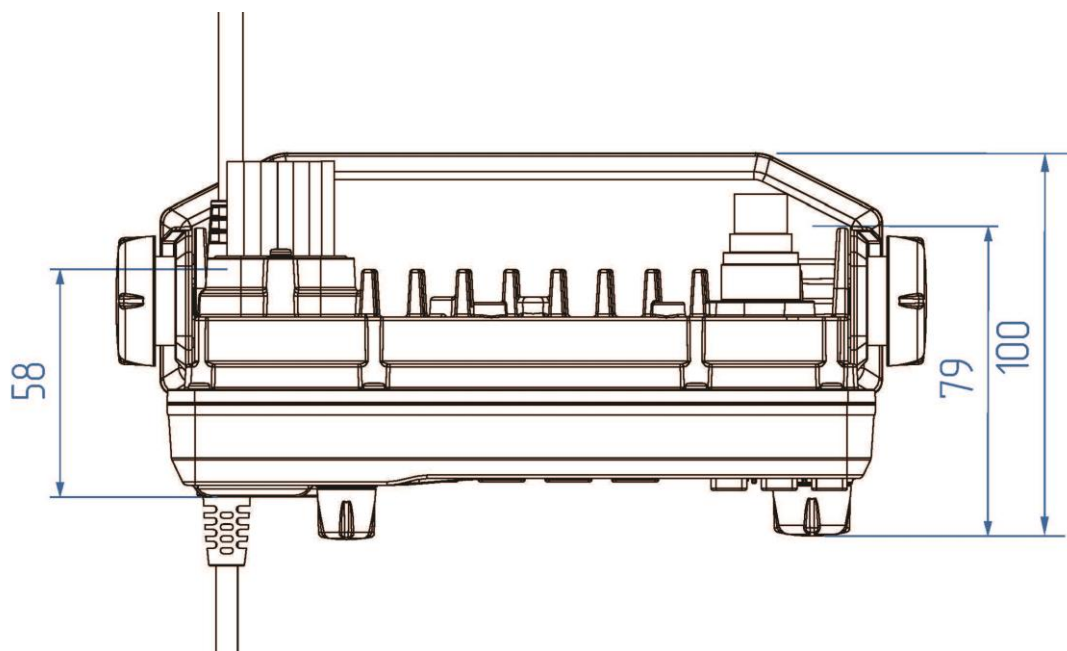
Габаритные размеры радиостанции (вид сверху)
